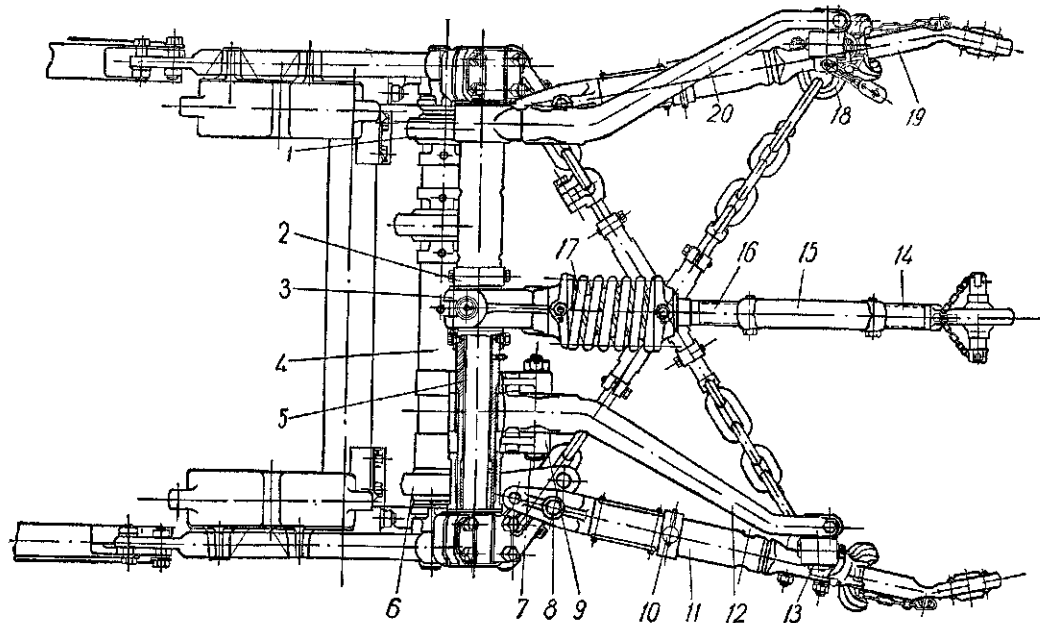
Механизм для навешивания орудий, установленный по трехточечной схеме:
